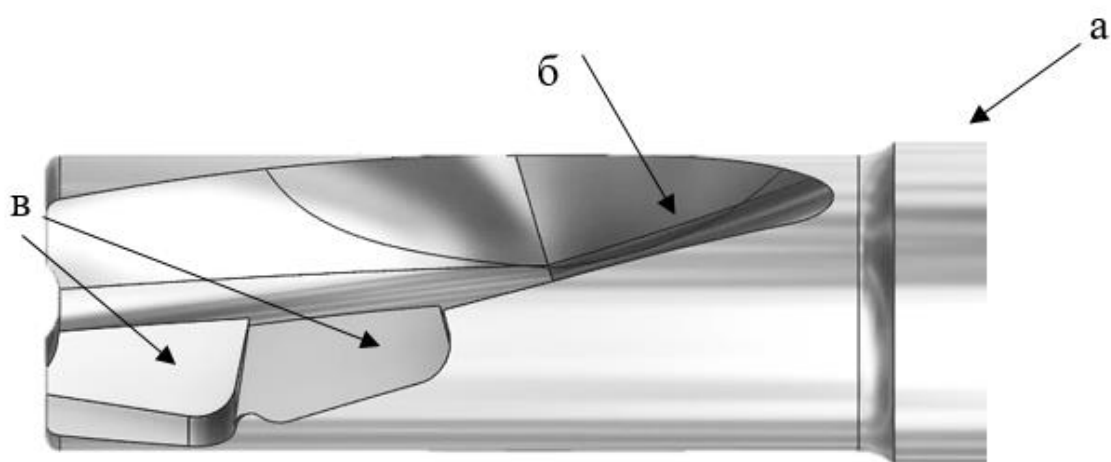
Корпус фрези: а - хвостовик, б – гвинтова канавка, в – пази під пластинки
